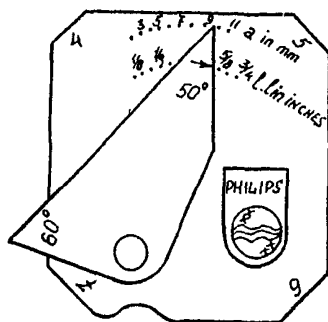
Шаблон для контроля сварных швов (фирма «PHILIPS»)
